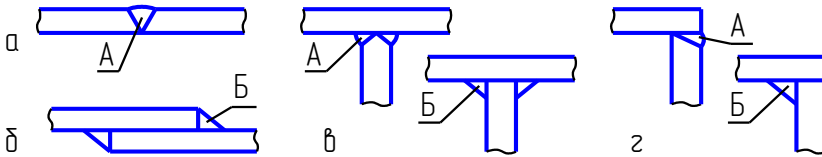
Види зварних з'єднань і типи зварних швів
